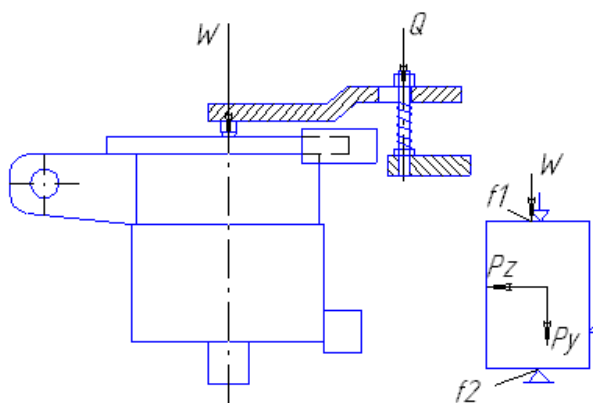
Розрахункова схема силового затиску заготовки
